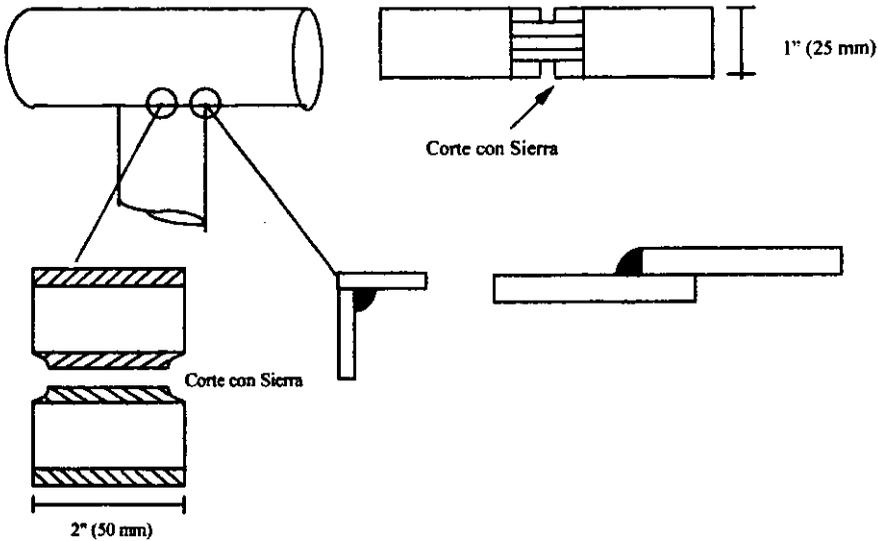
Localización de las Probetas para la Prueba de Sanidad: Soldaduras para Prueba de Calificación de Soldador y de Procedimiento en Soldaduras de Filete, incluyendo Prueba de Calificación de Soldador de Conexión de líneas del mismo diámetro.
